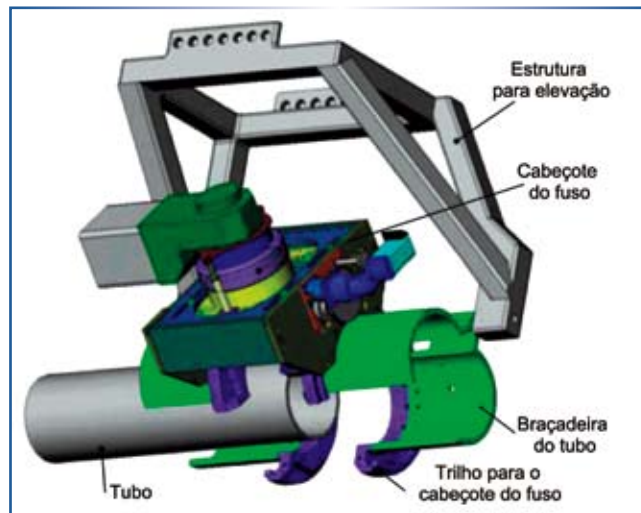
Equipamento para execução de soldagem circunferencial de tubos pelo processo de fricção linear⁽⁴⁾
